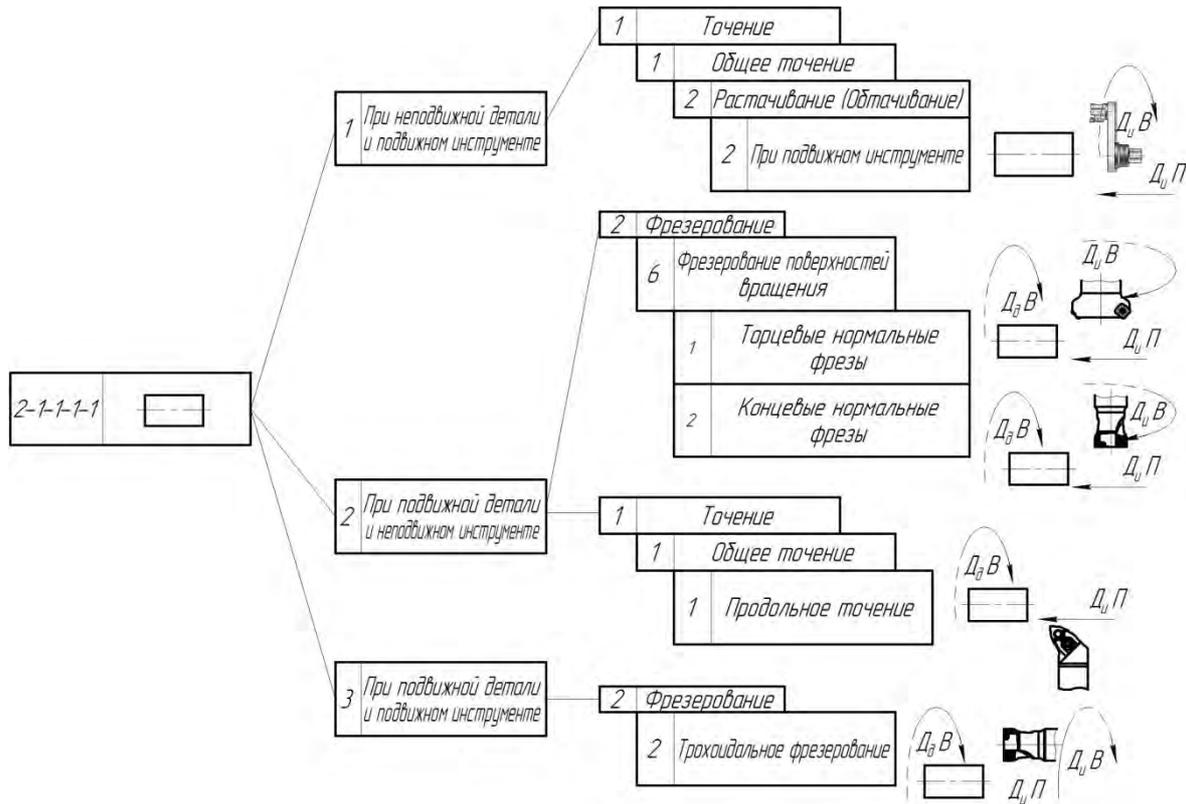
Пример формирования различных схем обработки цилиндрической ступени вала
